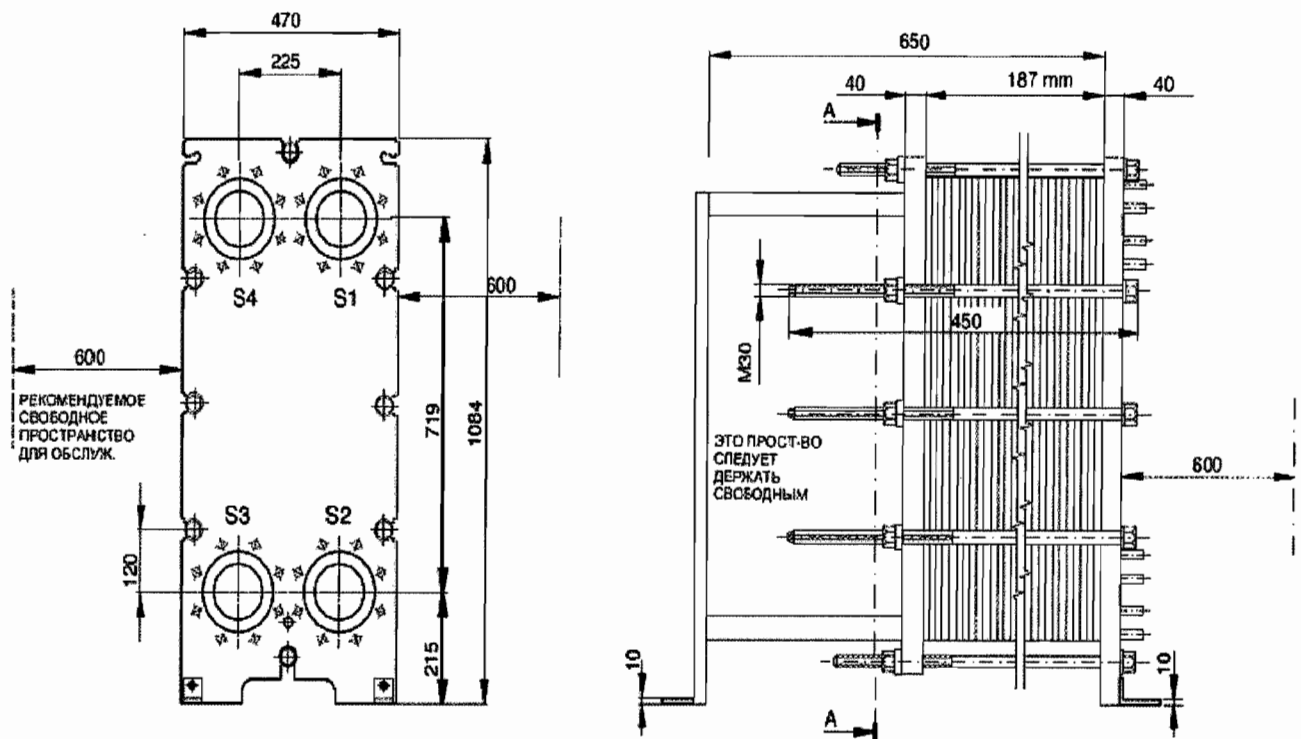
Габаритный чертеж охладителя выпара расширителя дренажей LCM01AC001
